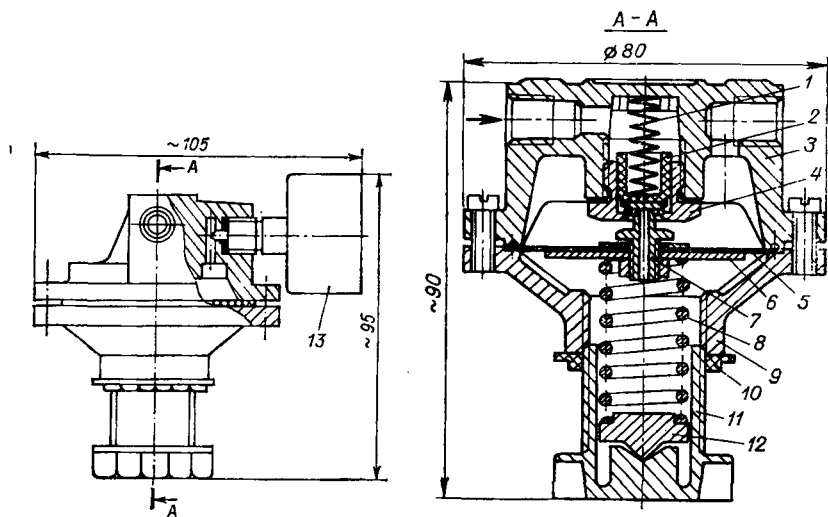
Стабилизатор давления воздуха СДВ-1,6М.
